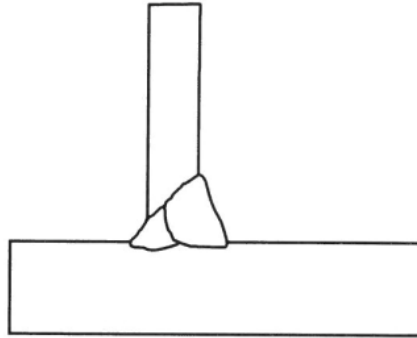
Geometrie der HV-Naht aus der Schweißanweisung [21]
